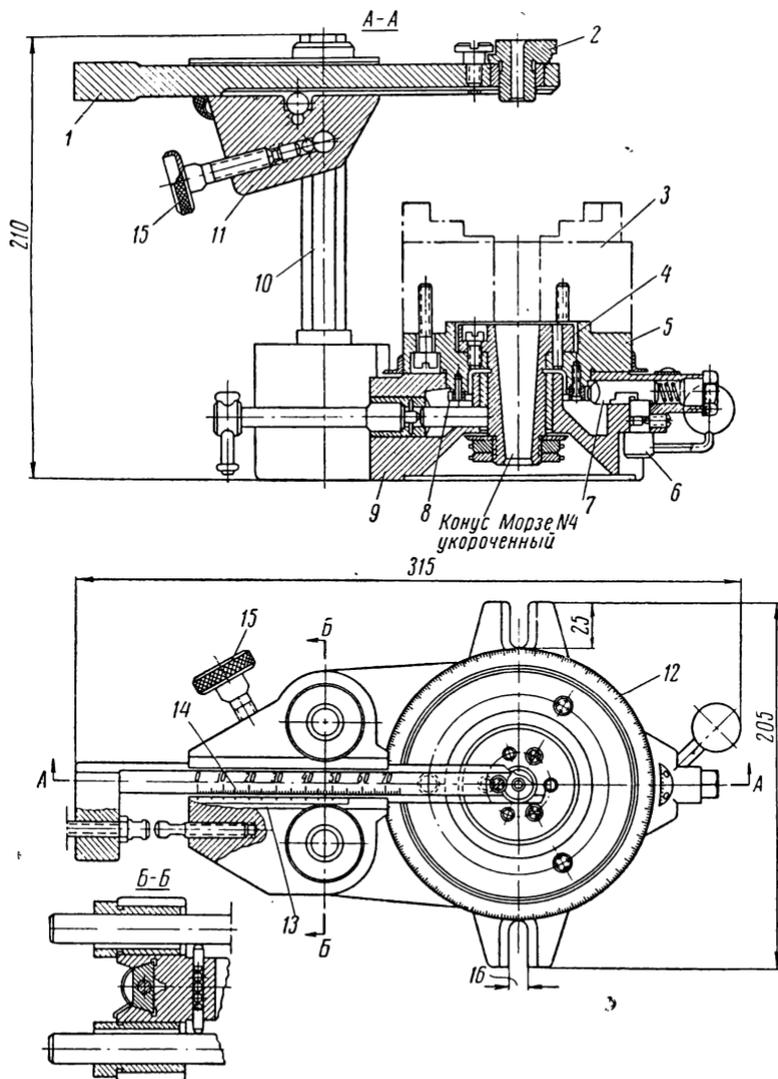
Групповой кондуктор для деталей типа фланцев, крышек, дисков
